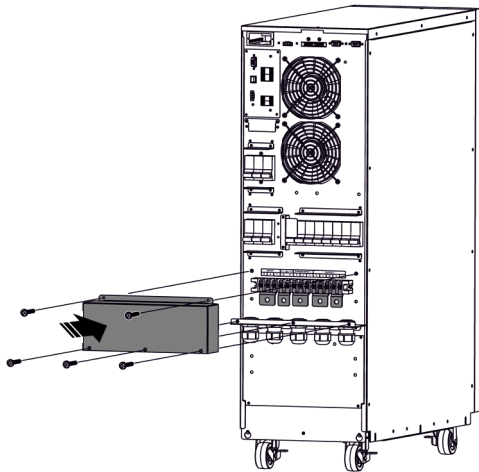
Remise en place du cache de protection des terminaux de connexion en version tour.
